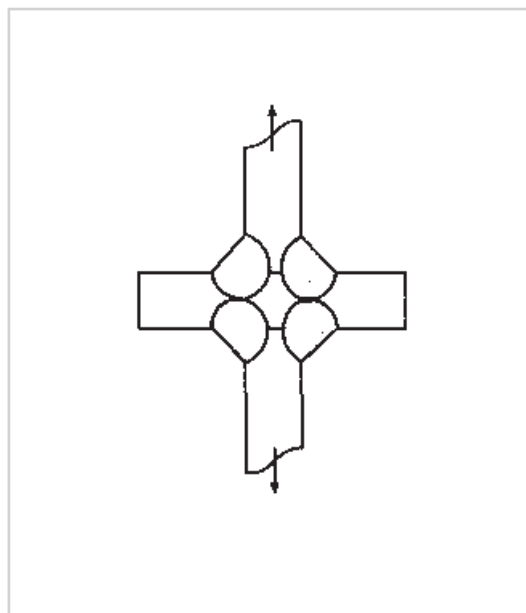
Схема фрагмента таврового сварного соединения с нумерацией ЗТВ (Кныш В. В., Кузьменко А. З., Соловей С. А. Повышение циклической долговечности сварных тавровых соединений с поверхностными трещинами // Автомат. сварка. — 2009. — № 1. — С. 38–43)
